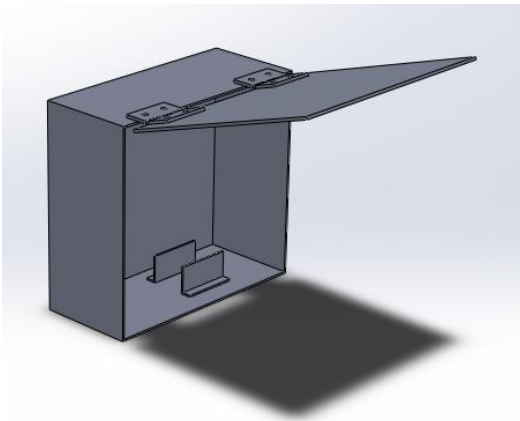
Diseño de la caja para el motor, válvula reguladora y sensor de presión
